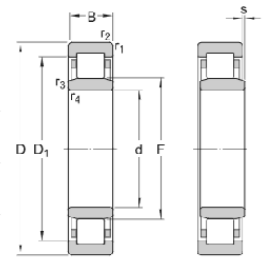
Dimensiones SKF NU 1016. Cortesía de SKF.
